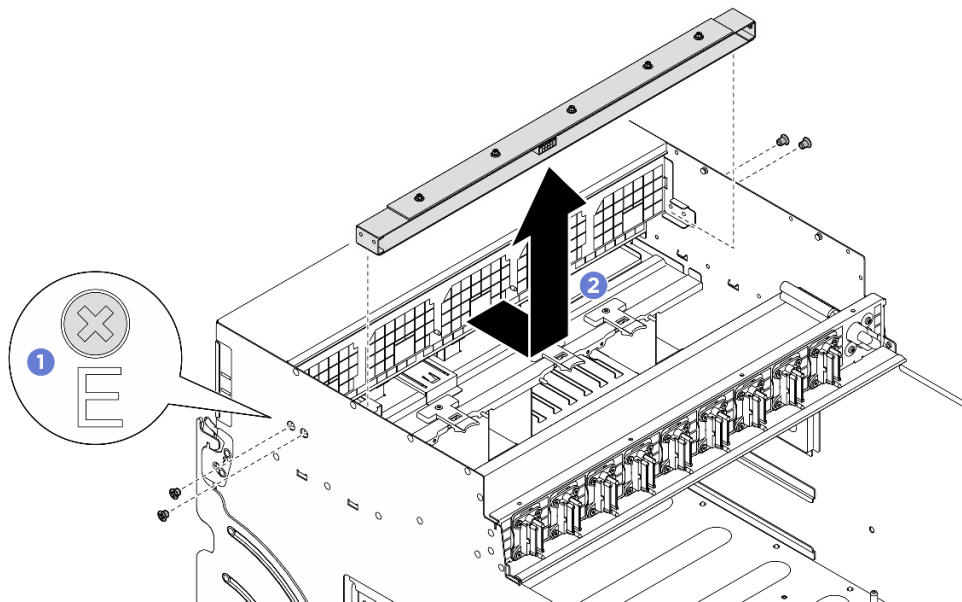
Remoção do conjunto de placa de controle do ventilador frontal
